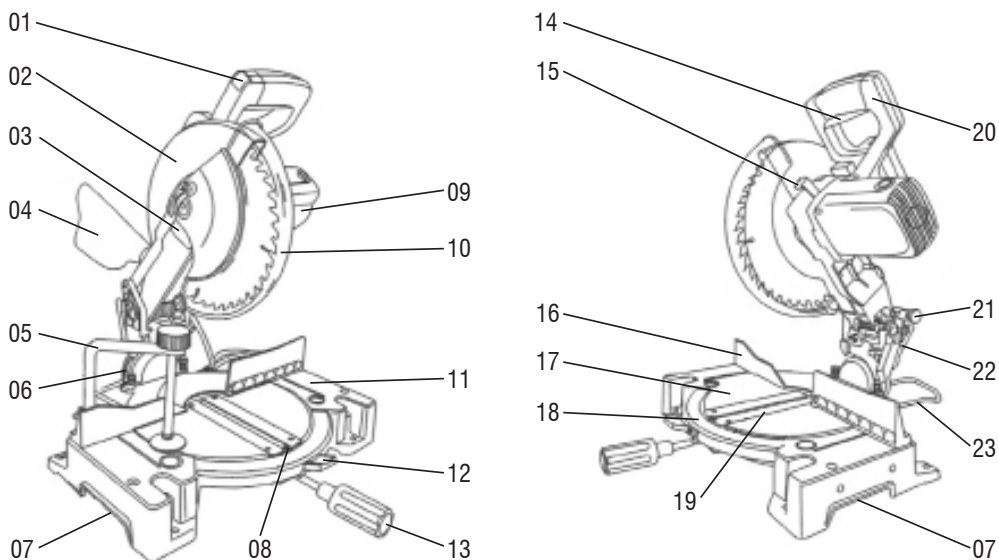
Componentes de la Sierra Acolilladora SEV 1600
